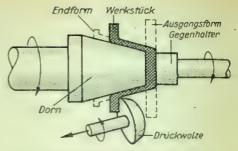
Projizierdrückwalzen (-streck-drücken)
